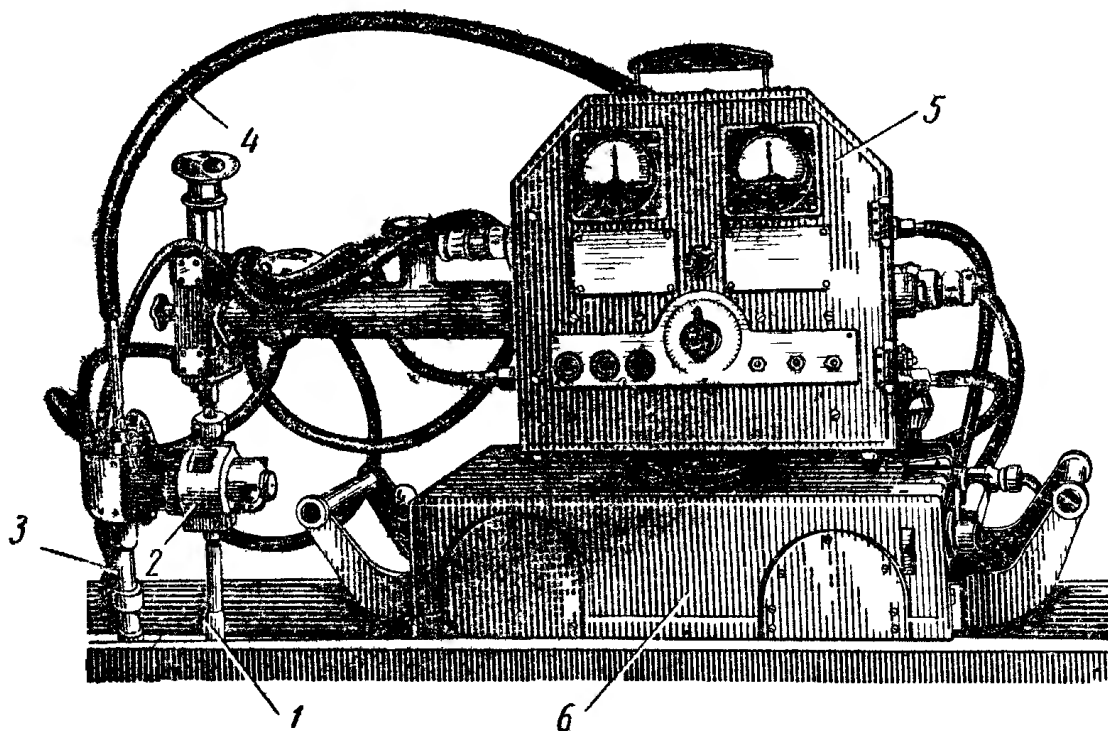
Установка УДС-58 для дуговой сварки в защитных газах
